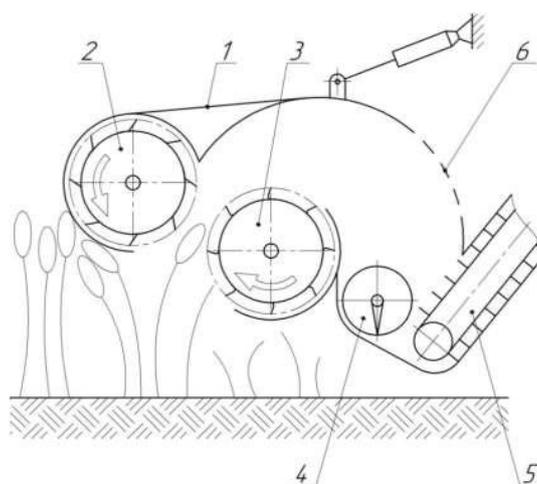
Пристрій для обмолоту сільськогосподарських культур на корені: 1 – корпус; 2 – подаючий барабан; 3 – барабан; 4 – шнек; 5 – плаваючий транспортер; 6 – сітчаста поверхня.
